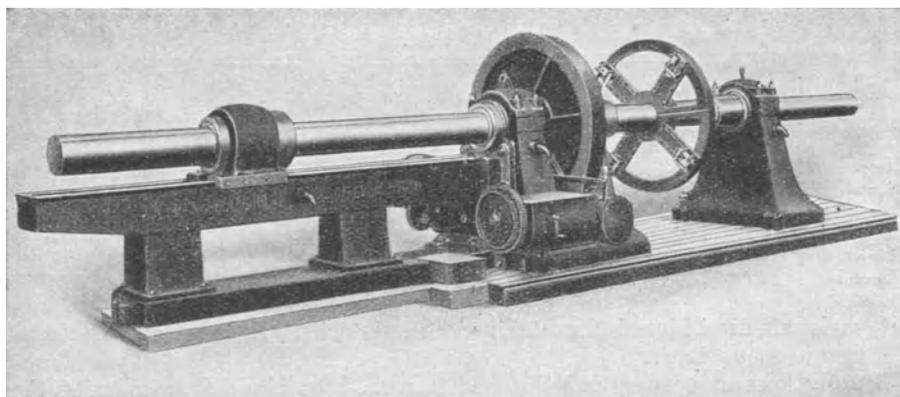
Maschine mit verschiebbarer Bohrstange.
